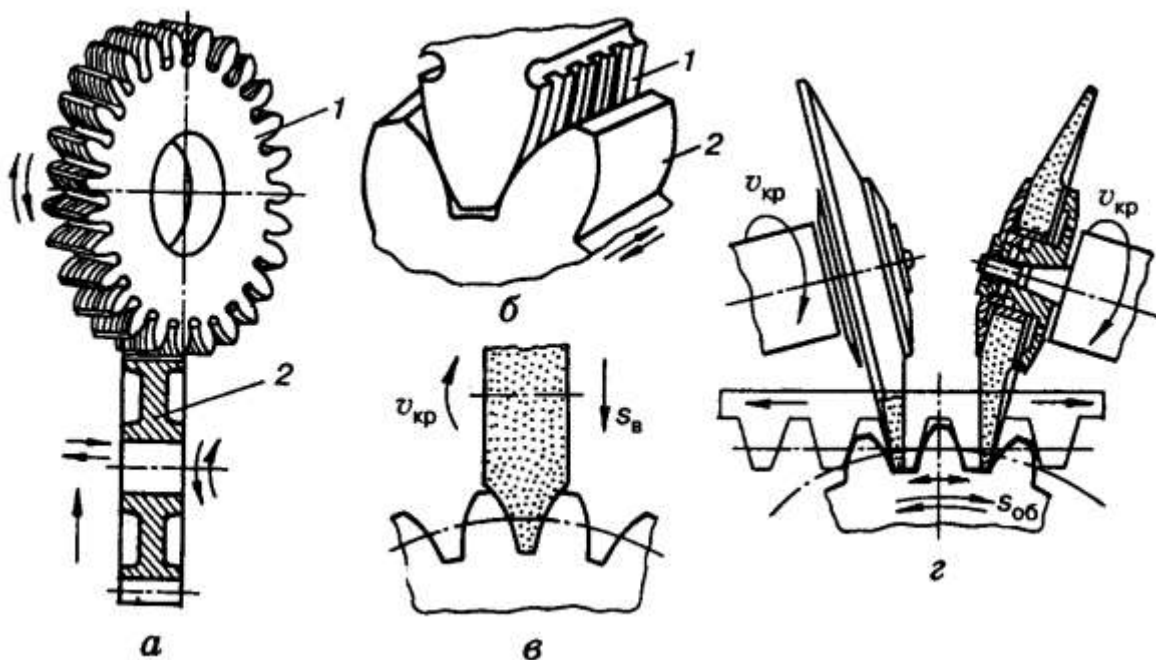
Схеми чистової обробки зубців зубчастих коліс
